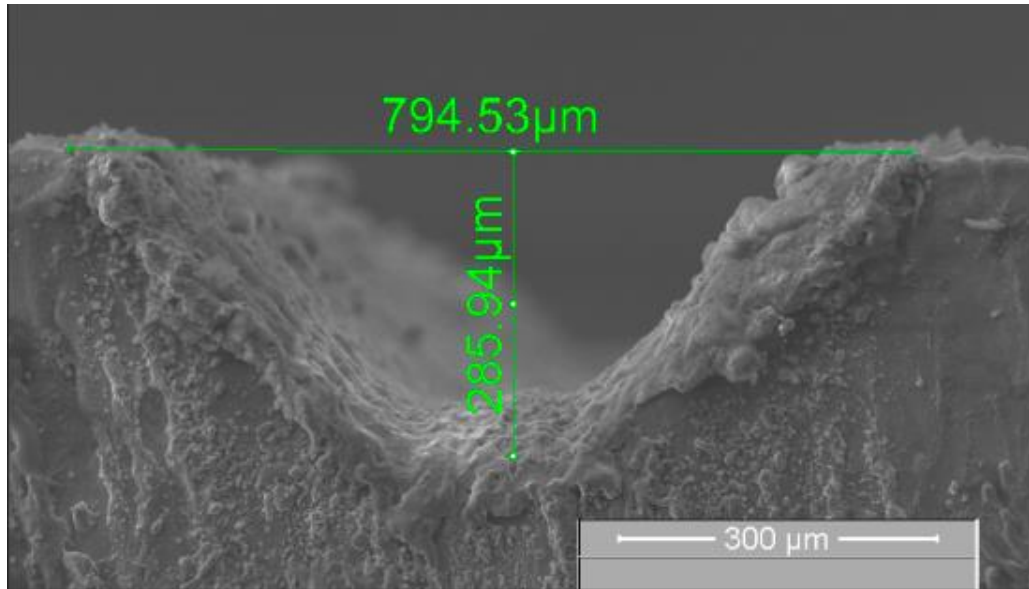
Торец образца из стали 12X18H10T с параметрами для получения резьбового соединения М3 с дополнительной обработкой финального слоя
